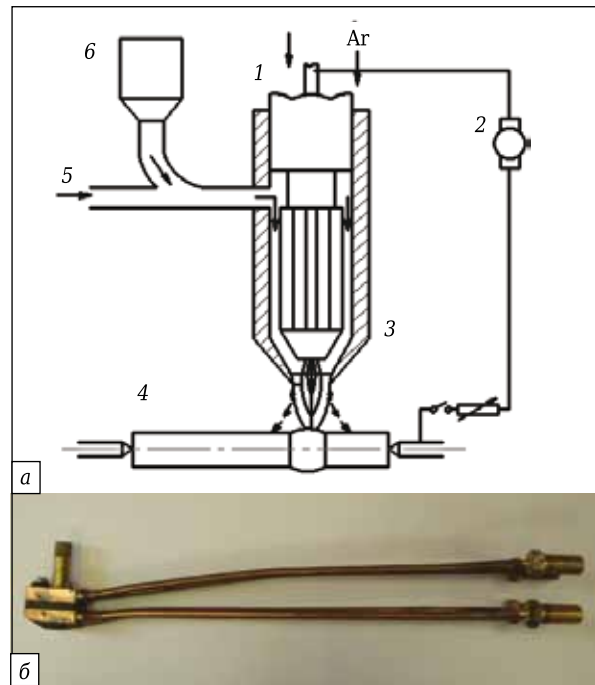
Схема плазменной наплавки (а) и малогабаритный плазмотрон (б) в защитной среде газопорошкового потока: 1 — корпус плазмотрона; 2 — источник тока; 3 — газопорошковая смесь; 4 — наплавляемая деталь; 5 — газ, транспортирующий порошок; 6 — порошковый питатель
